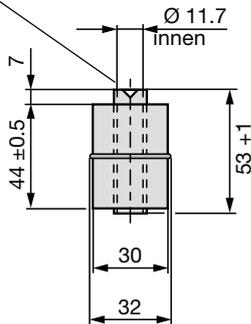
Abmessungen des Schwimmers BTL2-S-3212-4Z
